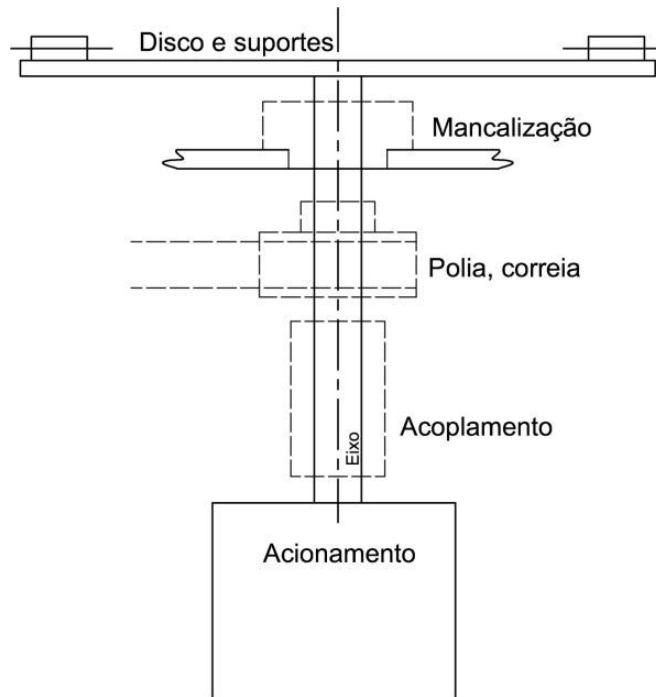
Croqui, vista lateral do sistema de eixo vertical
